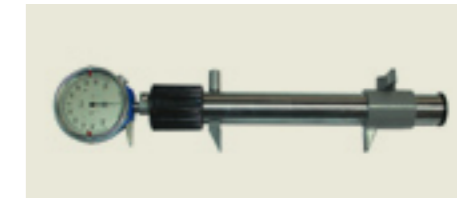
Нормалемер БВ-5045 для колес наружного зацепления
